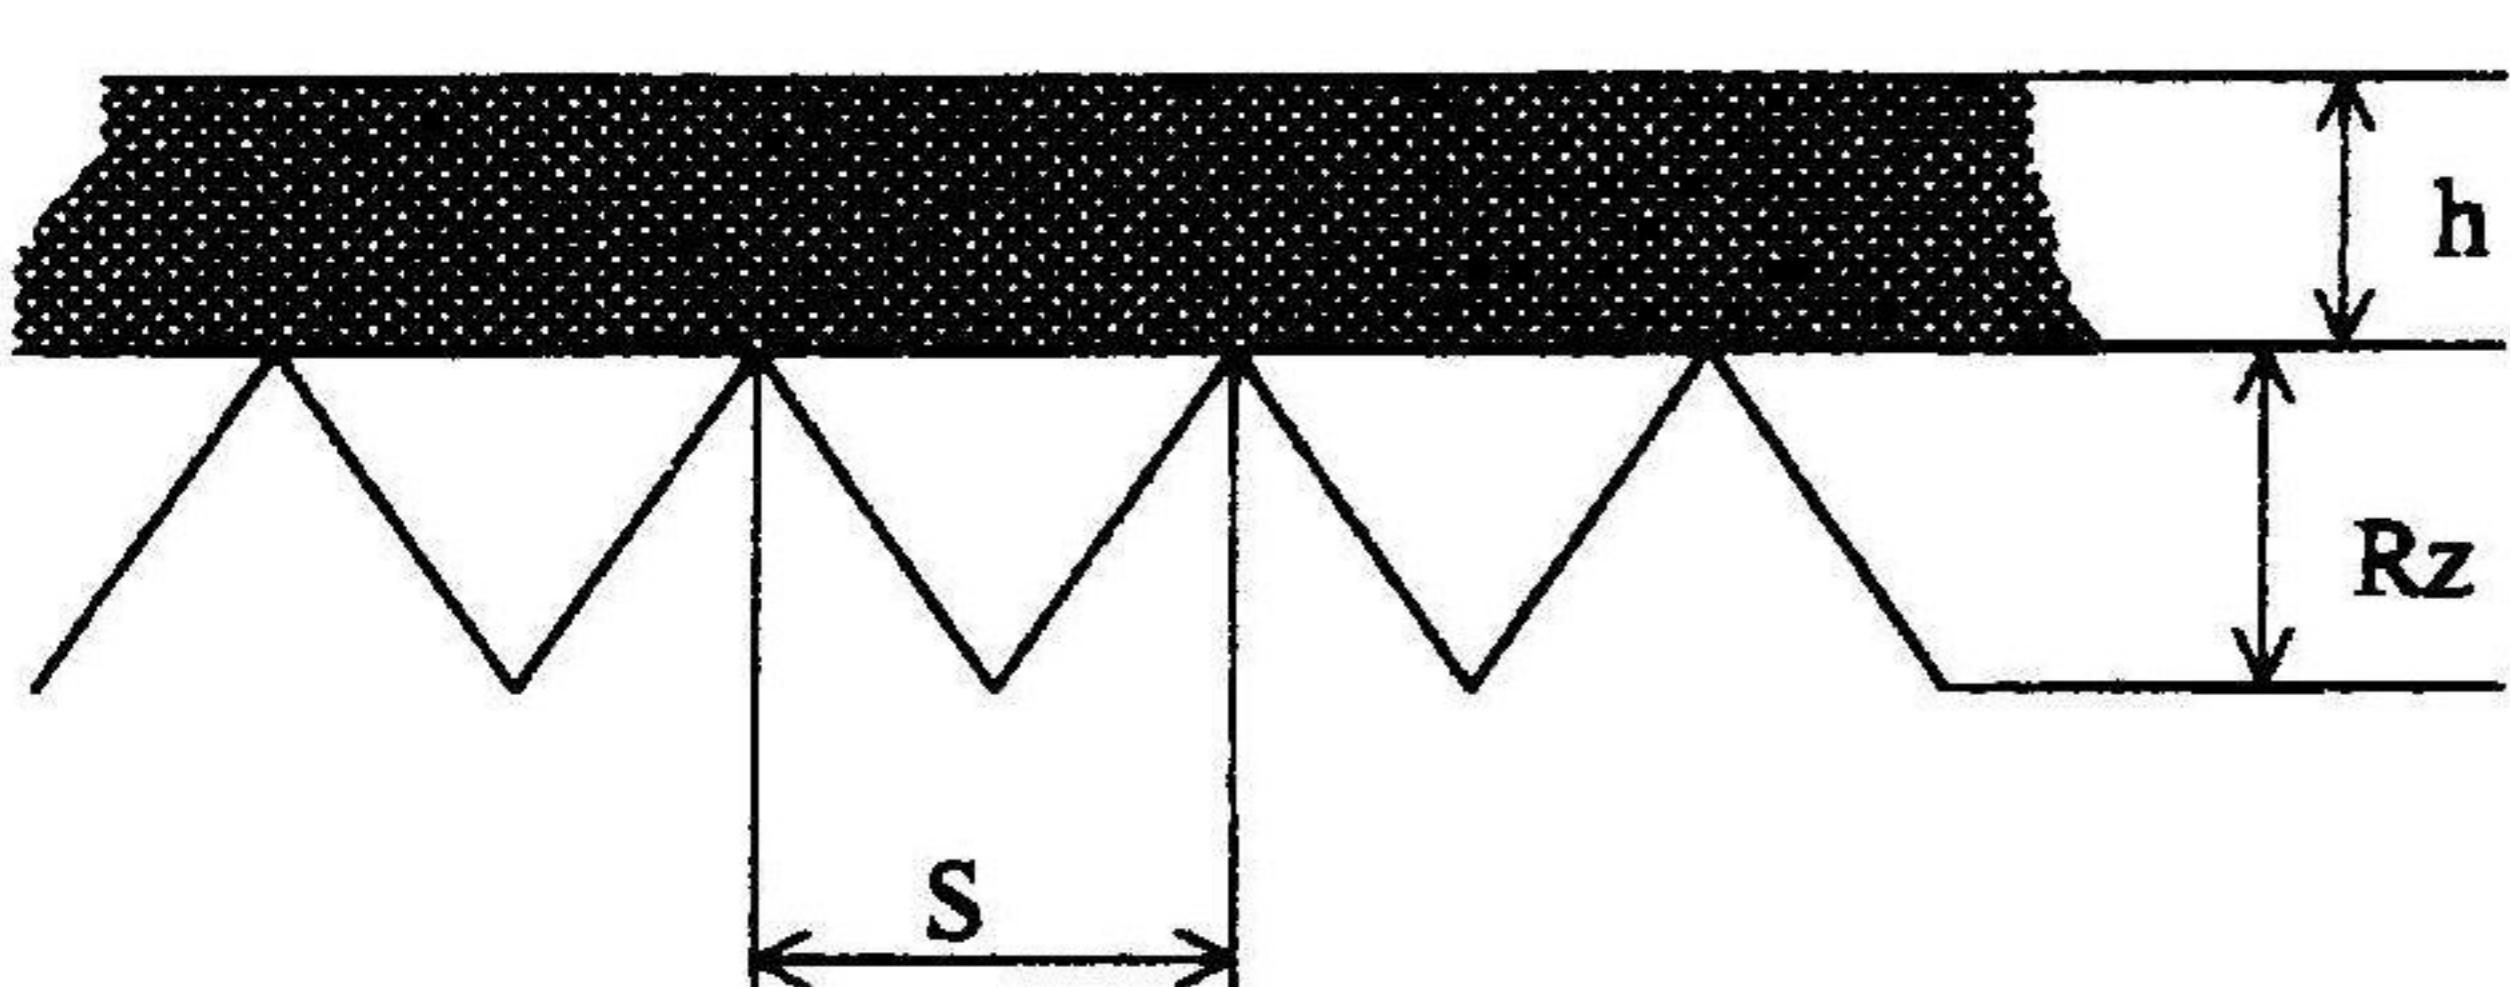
Положение пленки на шероховатой поверхности барабана.
